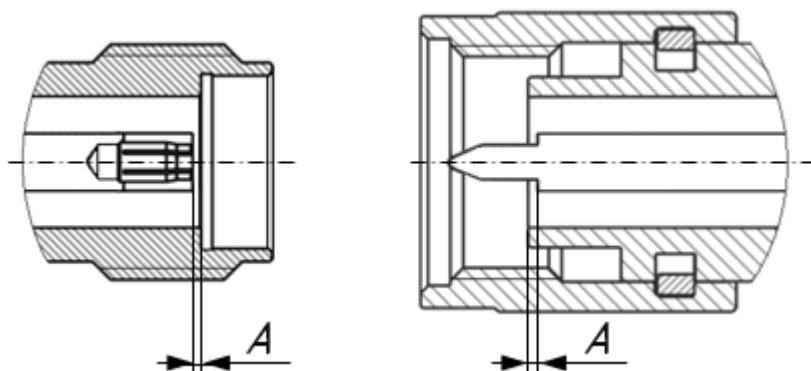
Соединители тип 3,5 мм (розетка и вилка)
